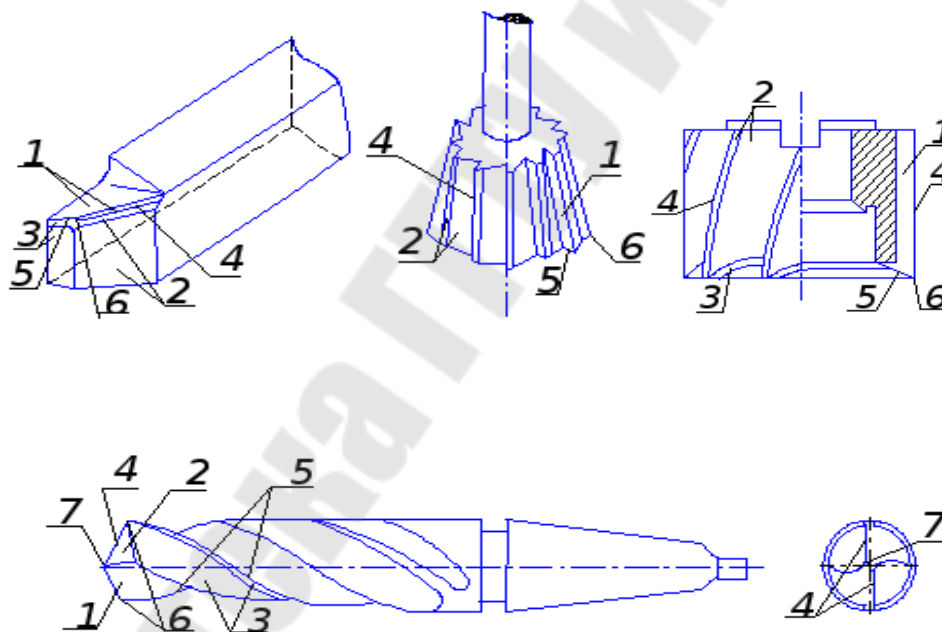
Поверхности и кромки на рабочей части лезвийных инструментов: 1 – передние поверхности; 2 – главные задние поверхности; 3 – вспомогательные задние поверхности; 4 – главные режущие кромки; 5 – вспомогательные режущие кромки; 6 – вершины; 7 – поперечная кромка (перемычка)
